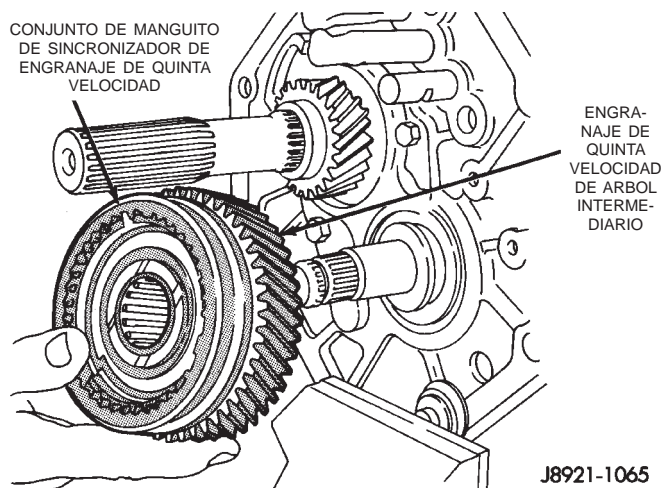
Desmontaje de conjunto de sincronizador y engranaje de quinta velocidad
